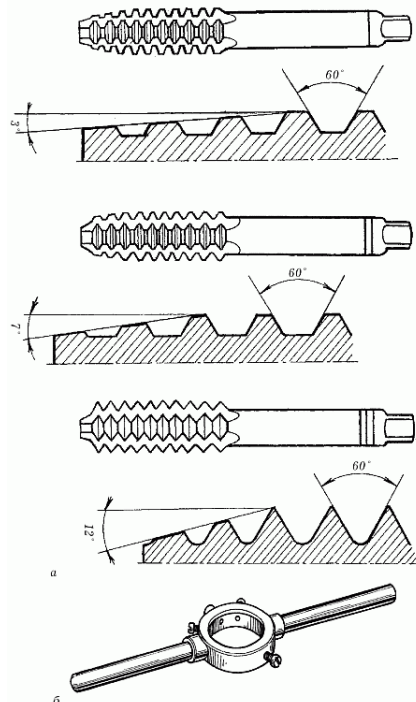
Инструменты для нарезания внутренней резьбы: а – метчики; б – вороток
